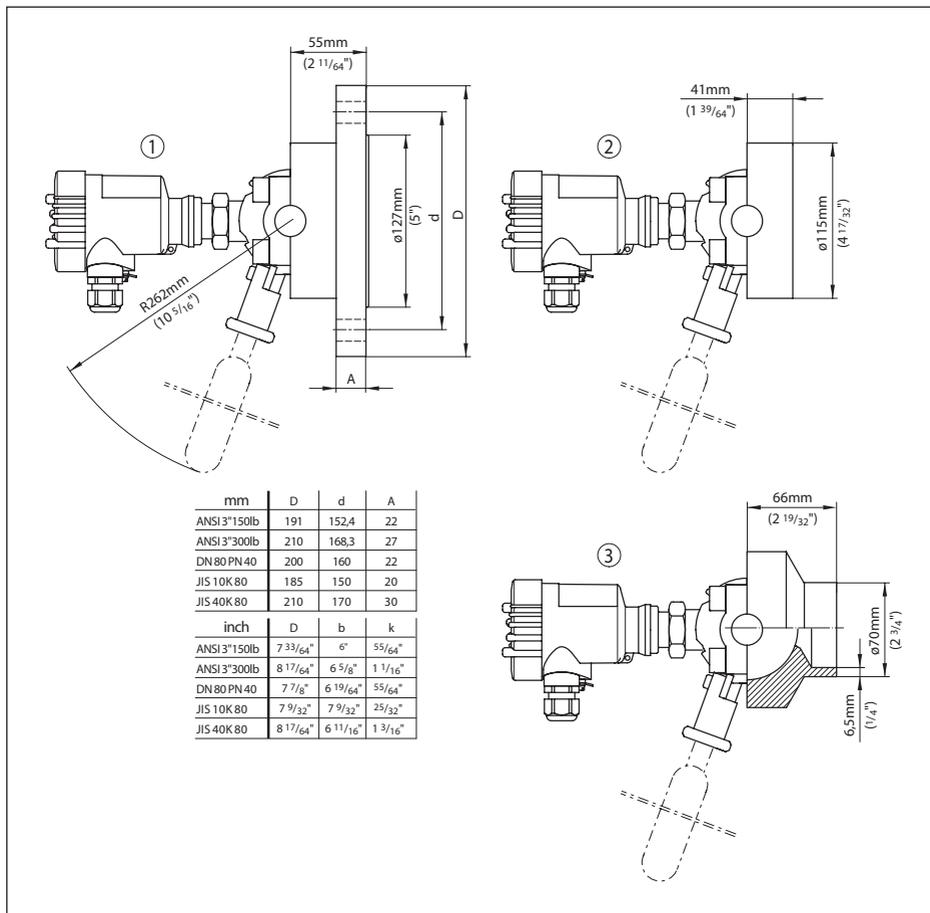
Dispositivo di montaggio a valvola sferica PASVE
